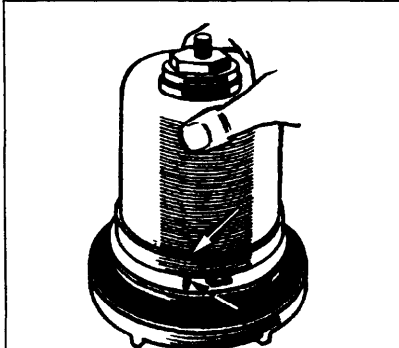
Установка колпака ротора центробежного фильтра очистки масла по установочным меткам
